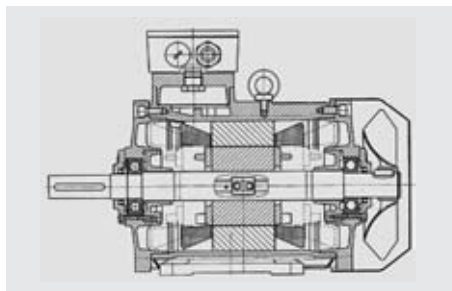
CORTE DE UN MOTOR TRIFASICO
